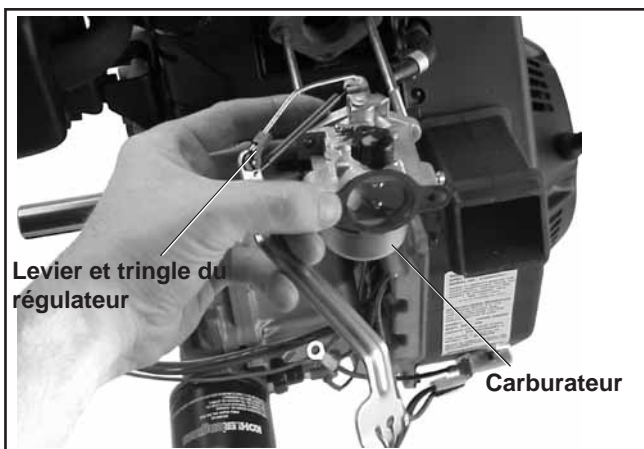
Retirer le carburateur sans retirer le levier du régulateur.
